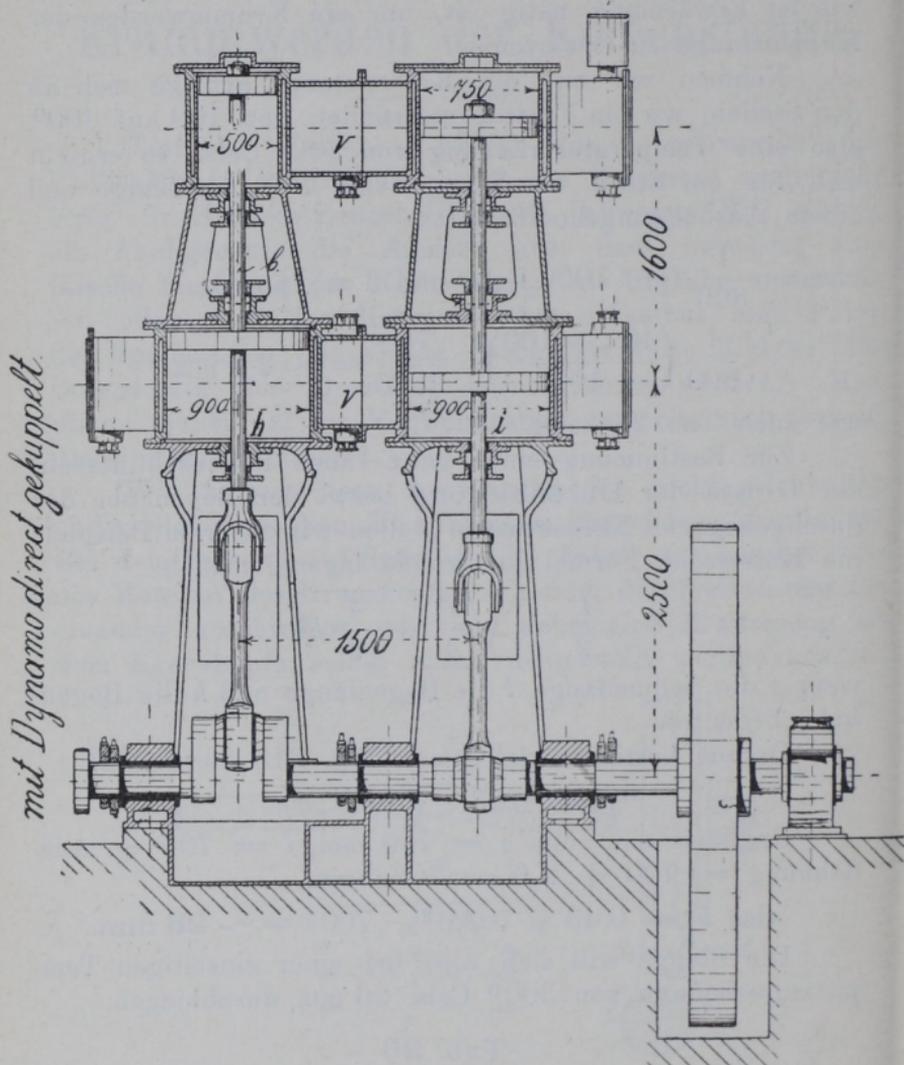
Dreifach-Expansionsmaschine. Massstab 1:40.
